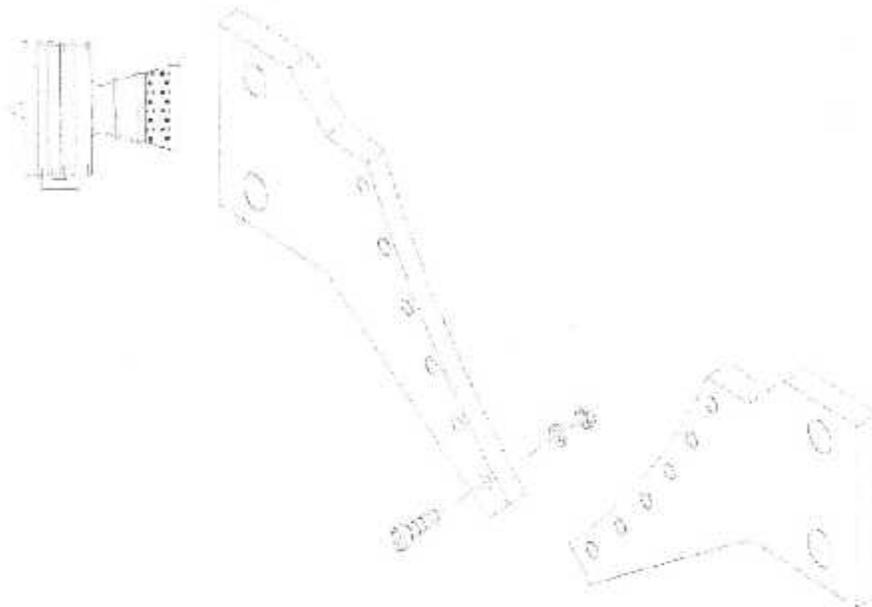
Ferrures d’Assemblage .865A1800G02
